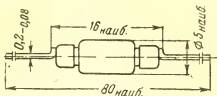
Габаритный чертеж диодов Д11—Д14А.
